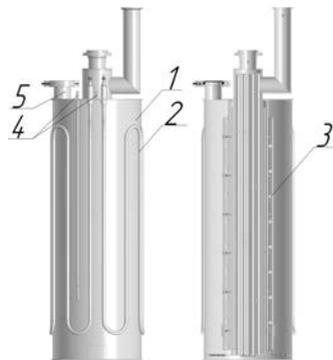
Основные составные части конвертера: 1 – камера герметичная; 2 – внешний нагреватель типа ТЭН; 3 – внутренний спиральный нагреватель типа ТЭН; 4 – корпус термомпары; 5 – фланец для засыпки наполнителя
